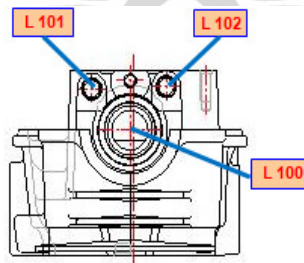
Proses OP 50 *Cylinder Head Machining
